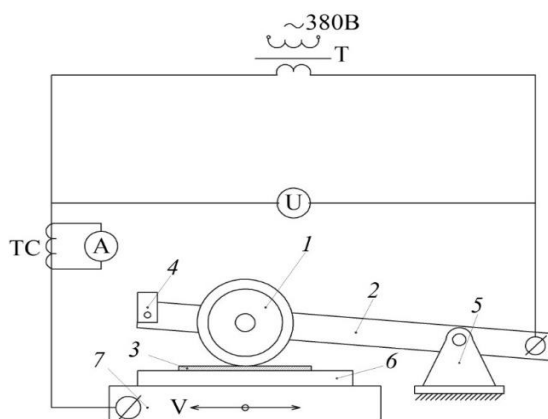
Схема установки для формування на сталевій поверхні високовуглецевого шару
